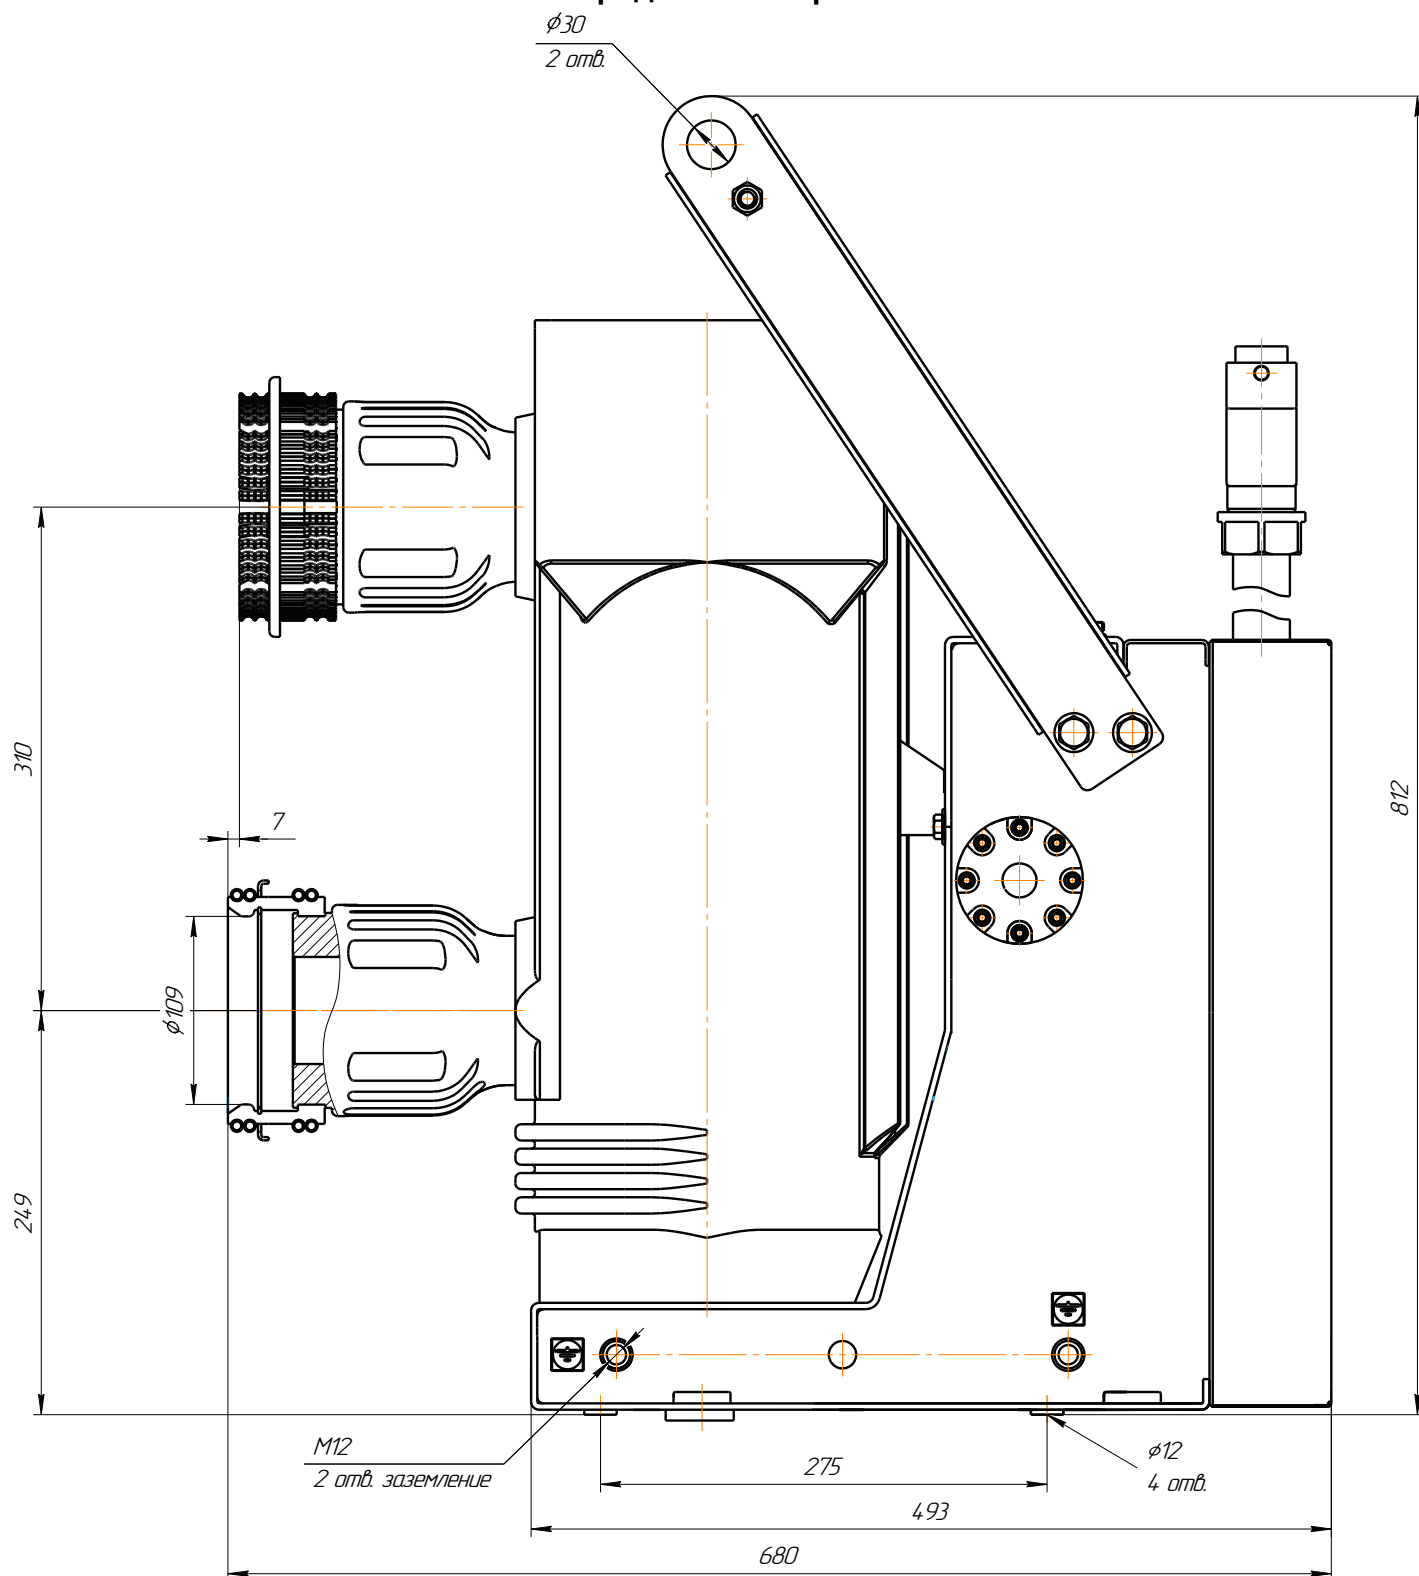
Габаритные и присоединительные размеры выключателя ВБУ-СЭЩ-10-50
